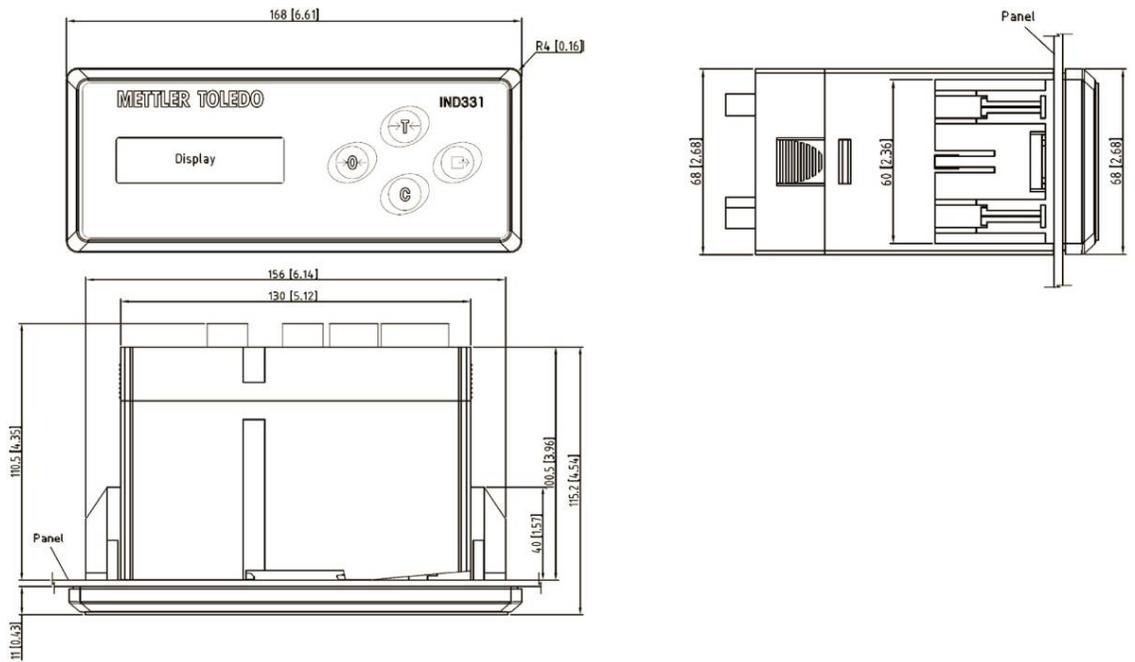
Dimensões do gabinete do IND331 para montagem em painel
